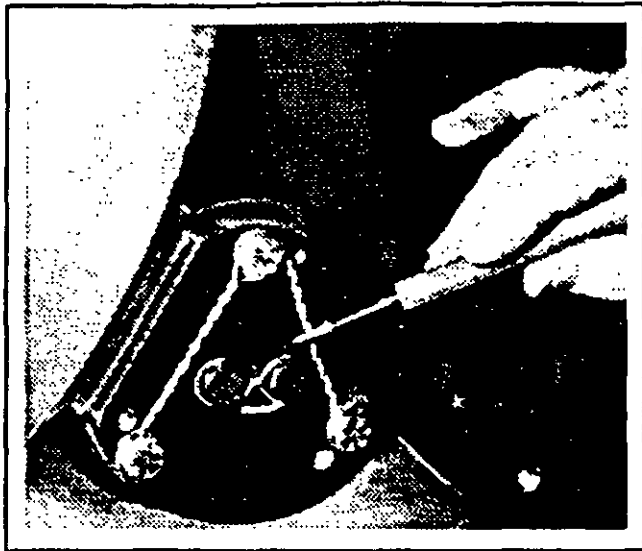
APLICANDO ALAMBRE CANDADO A LOS TORNILLOS DEL ENGRANE LUBRICADOR. E-24258-S
